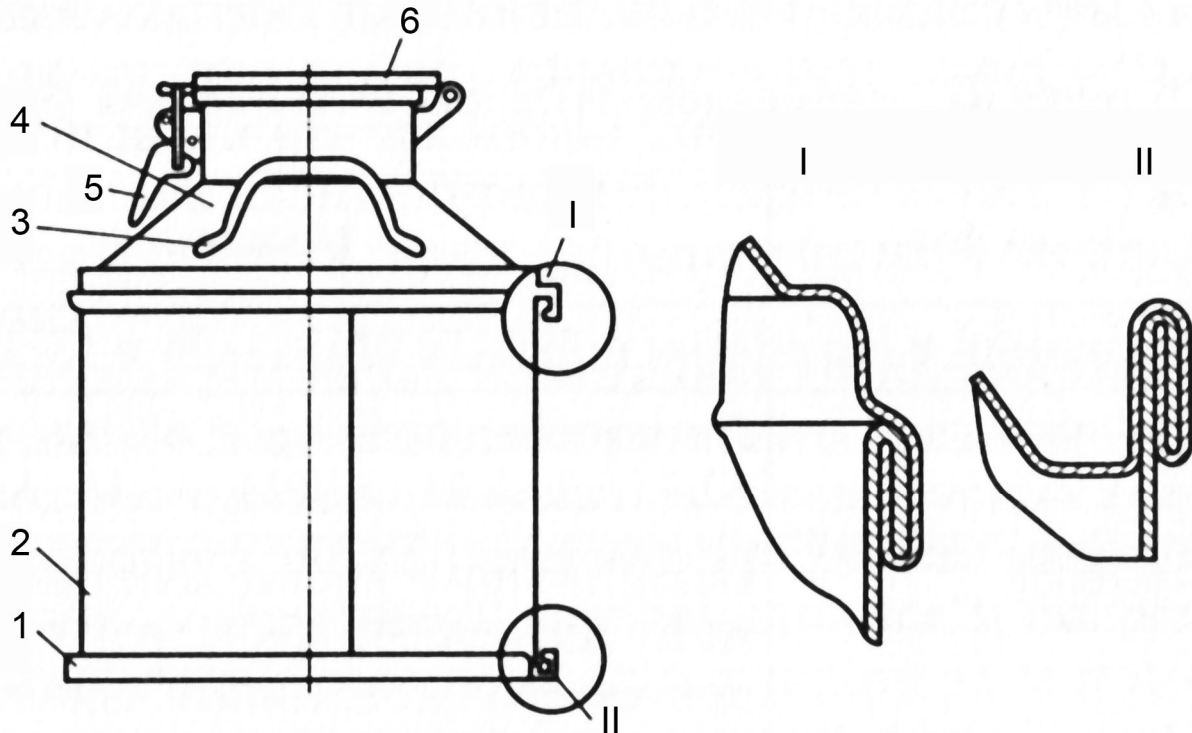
Конструкція сталеві фляги: 1 — днище;
